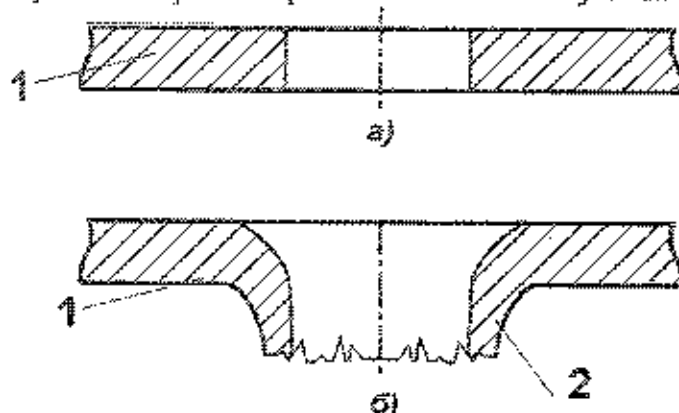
Отбортовка с предварительной пробивкой отверстия: а) до пробивки, б) после пробивки; 1– заготовка, 2– борт; [4]
